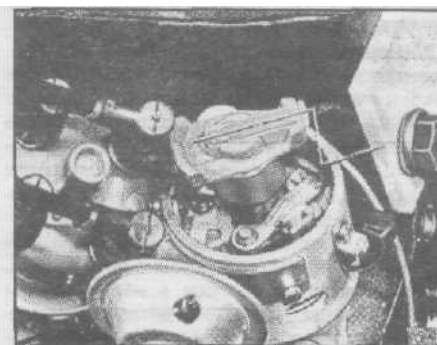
, в. Бегунок, совмещенный с меткой верхней мертвой точки на корпусе распределителя - двигателя 1,6 и 1,8 литра
